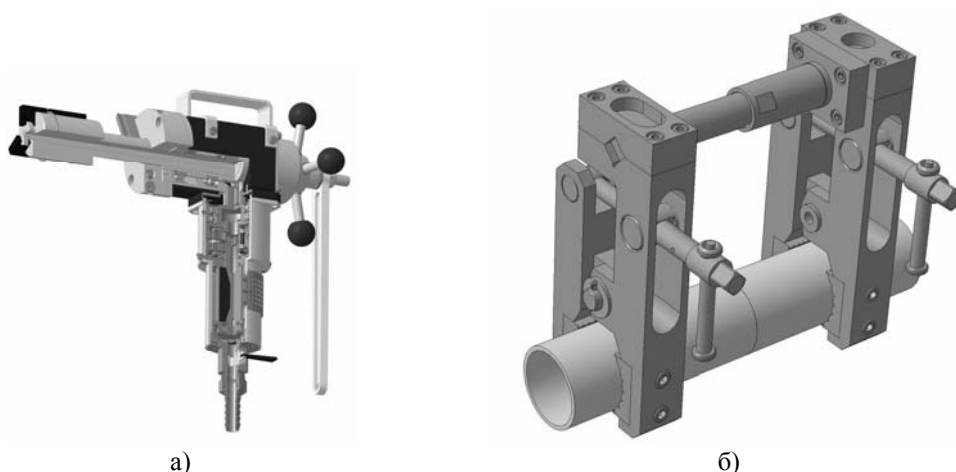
Механическое оборудование для подготовки и сборки под сварку стыков труб диаметром 57□219 мм:
